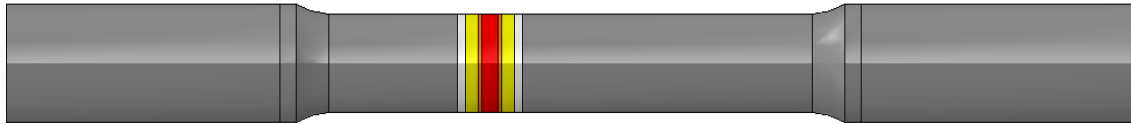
Position et composition de la soudure sur l'éprouvette
